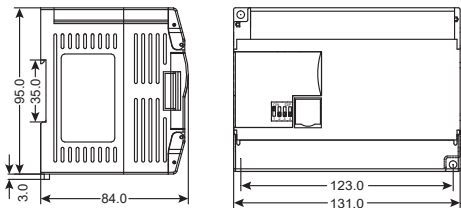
Габаритные размеры модулей REMF-D-40X, REMF-D-36Y-R, REMF-D-36Y-N
